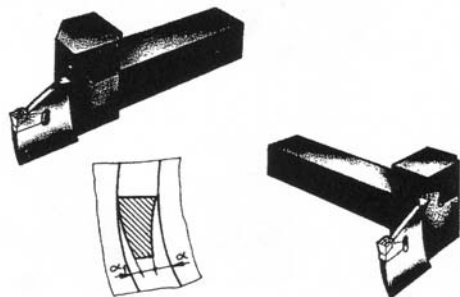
Forma de la herramienta en el ranurado frontal.
